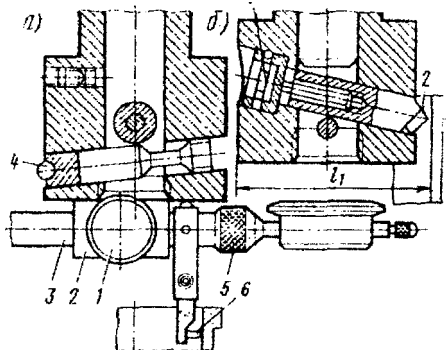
Резцовая головка станка 2А78Н с приспособлениями для центрирования цилиндра (а) и установки резца (б).
